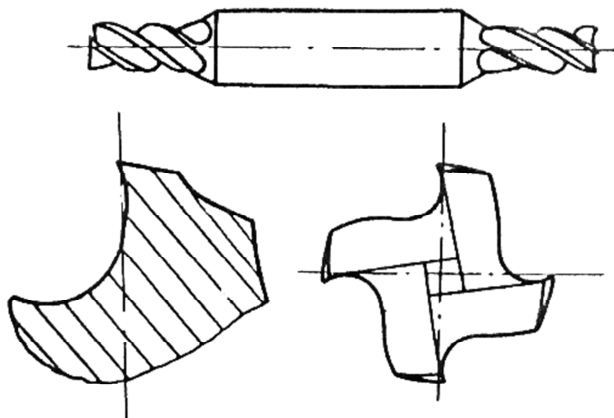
Концевая специальная фреза для изготовления полузакрытых пазов для СМП
